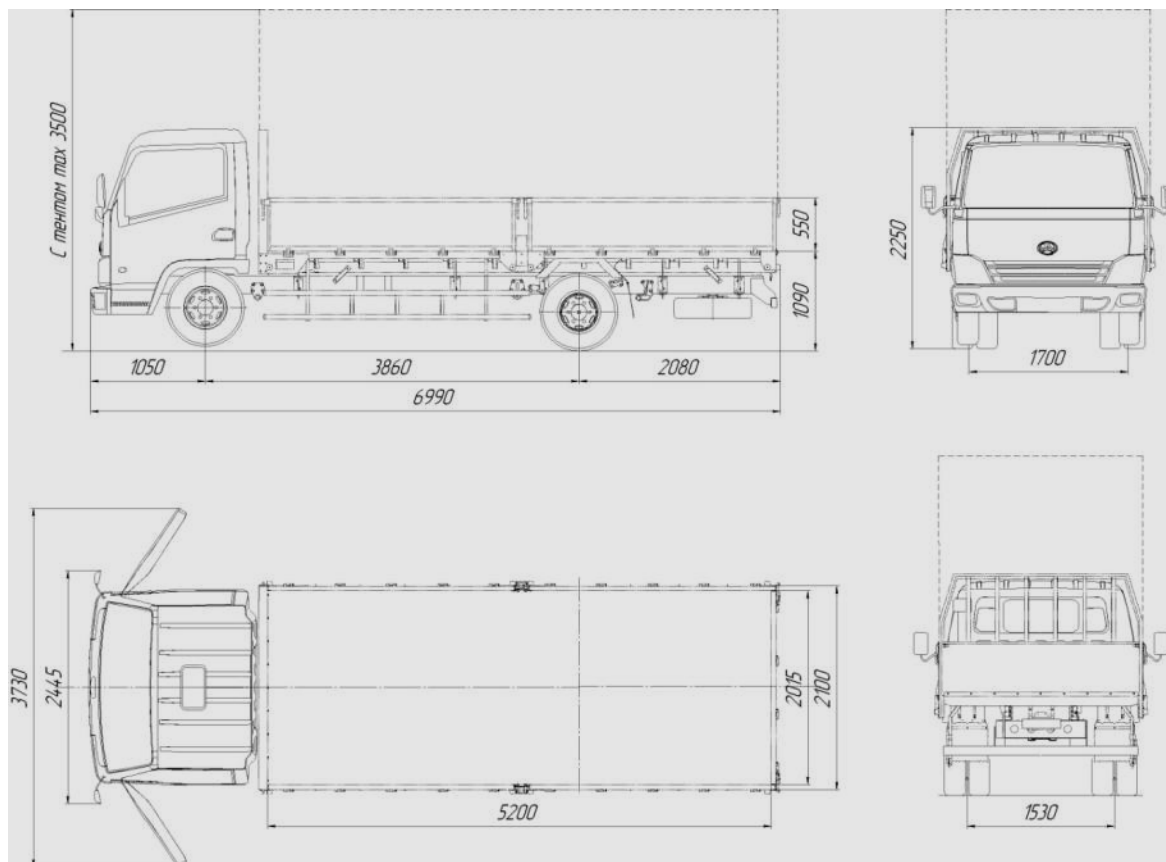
Автомобиль BAW 33460-0000010-101
